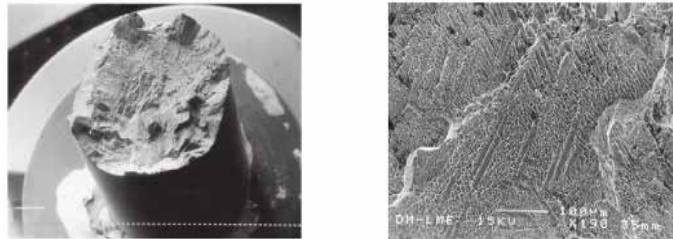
Fractura frágil macroscópica y detalle a mayores aumentos de la superficie de fractura.
